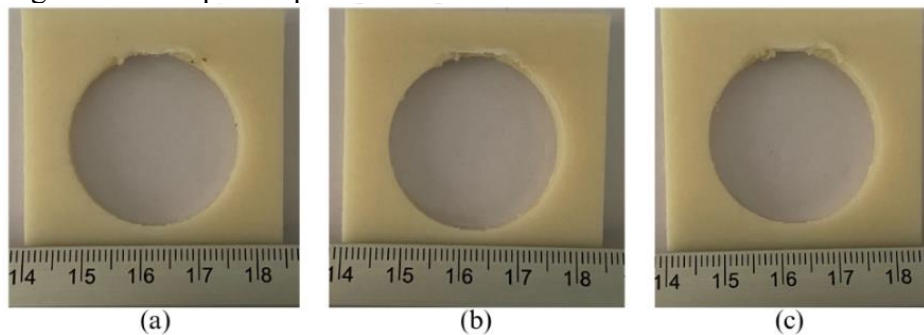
Corpo de prova impresso com destaque na parte superior do furo
